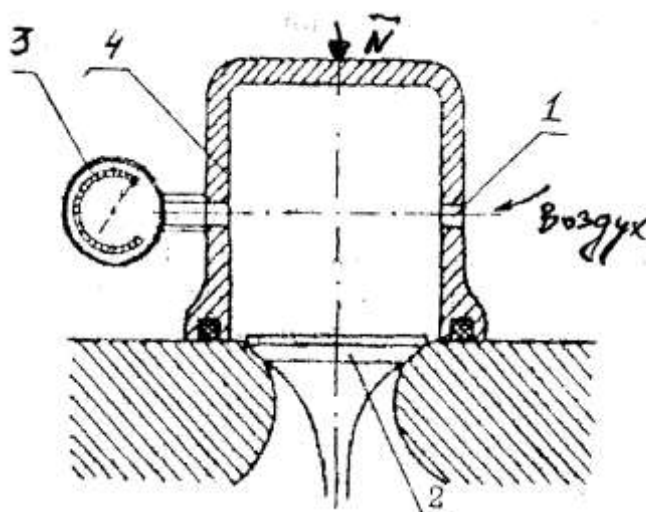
Проверка герметичности клапанов пневматическим приспособлением: 1 - отверстие для подвода сжатого воздуха; 2 - клапан, 3 - манометр; 4 - стакан приспособления.
